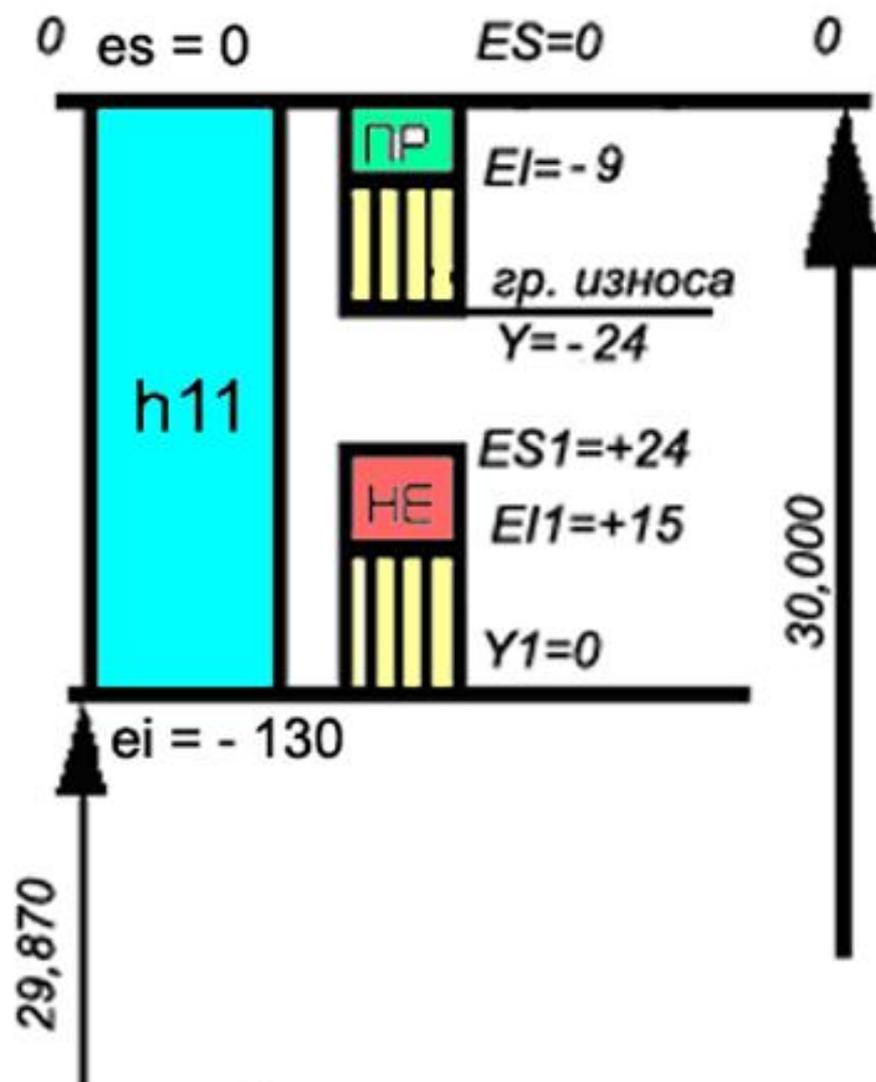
Схема полей допусков калибра, для контроля выступов по h_{11} .
